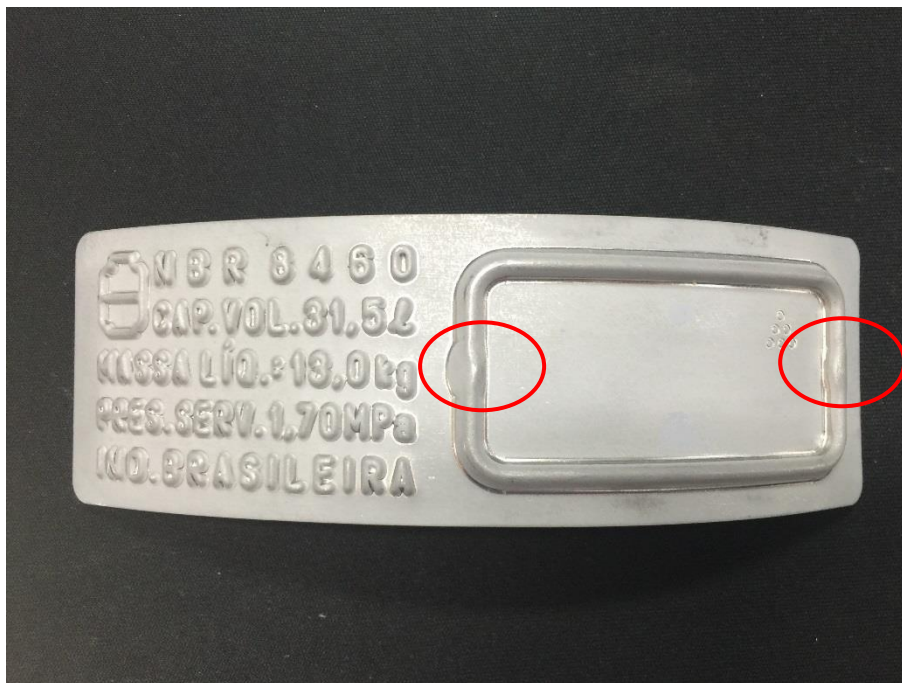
Modelo definido de moldura em alto-relevo, visando destaque e proteção da Plaqueta de Tara e posição de soldagem, no detalhe da moldura
